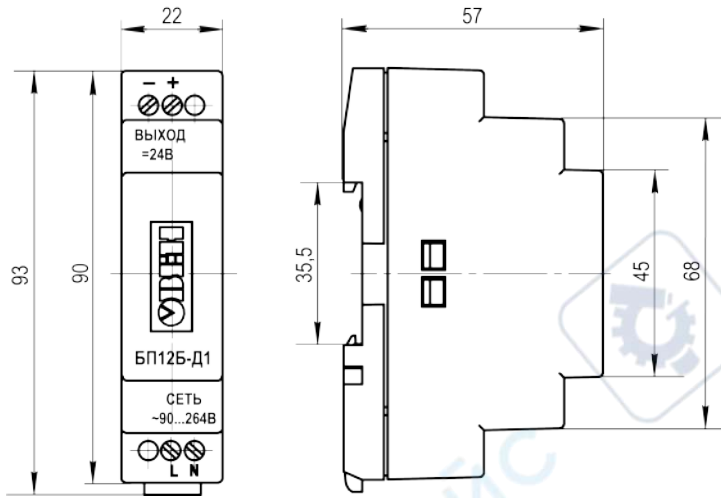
Внешний вид, габаритные и установочные размеры прибора
